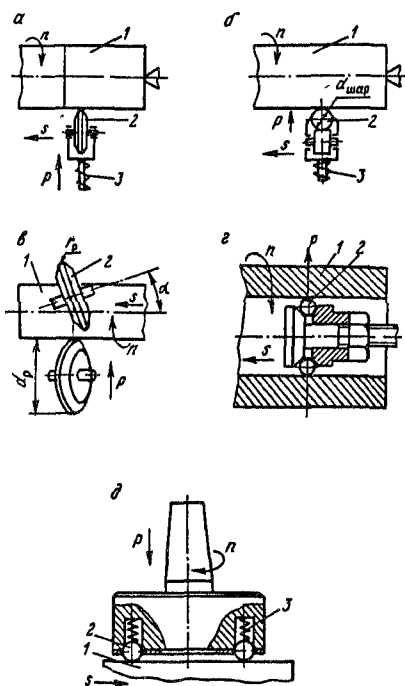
Схемы обработки способами ППД с качением инструментов: 1 — заготовка; 2 — инструмент; 3 — пружина
